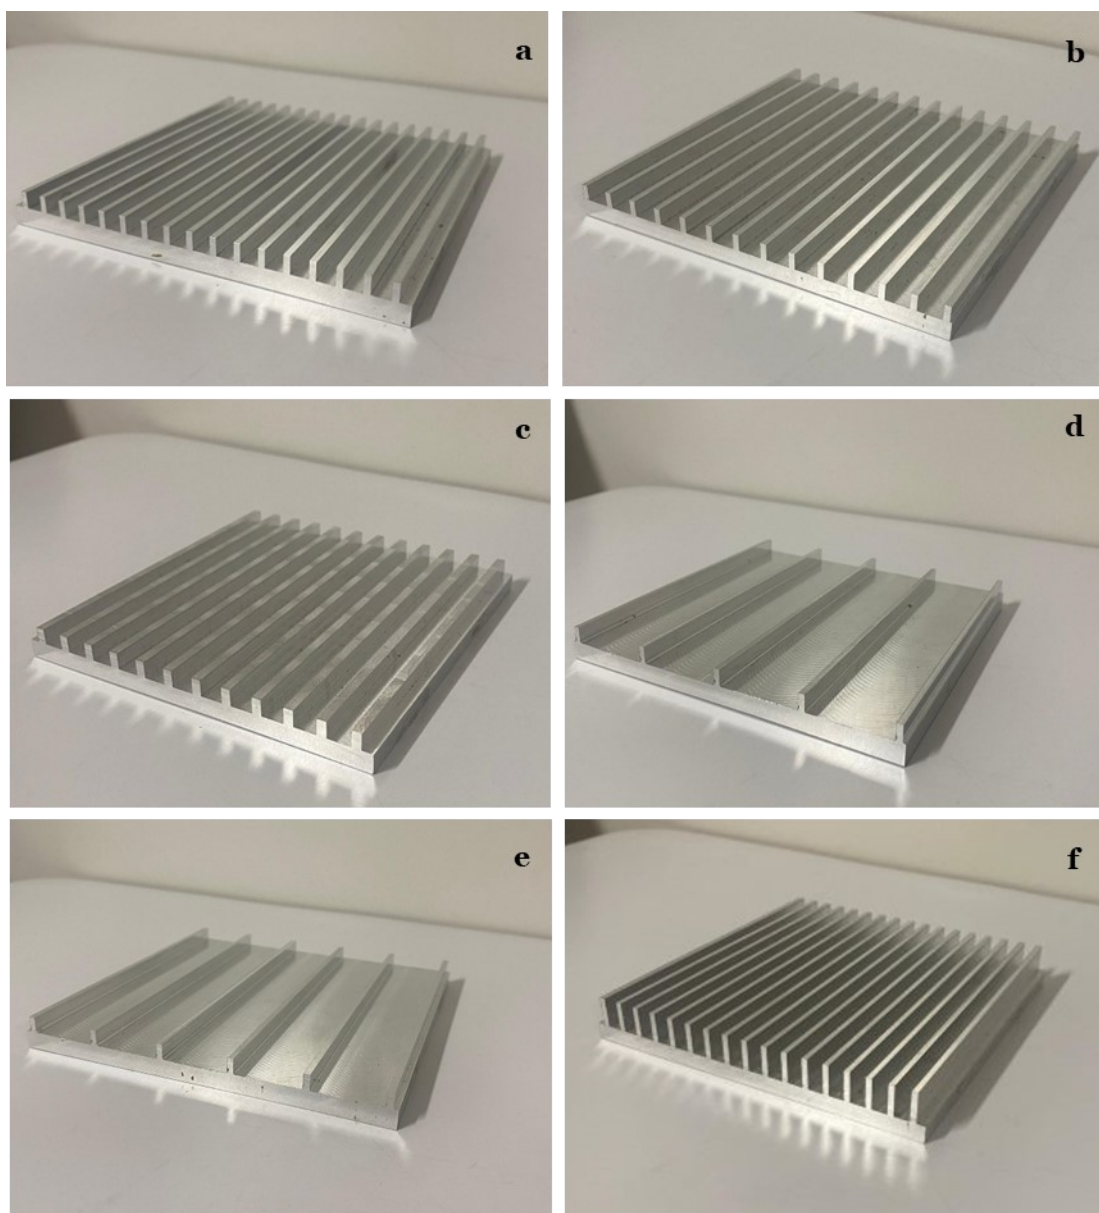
(a) Superfície A; (b) Superfície B; (c) Superfície C; (d) Superfície D; (e) Superfície E; (f) Superfície F.
